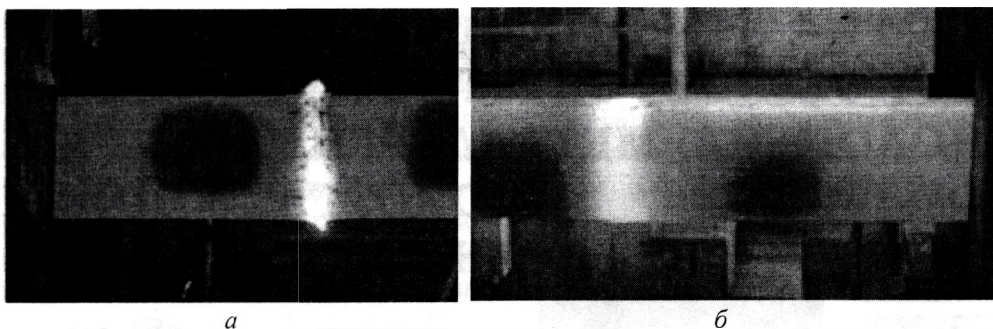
Сварка заготовок при бесконечной прокатке: а — сварной шов после соединения заготовок; б — сварной шов после обработки
